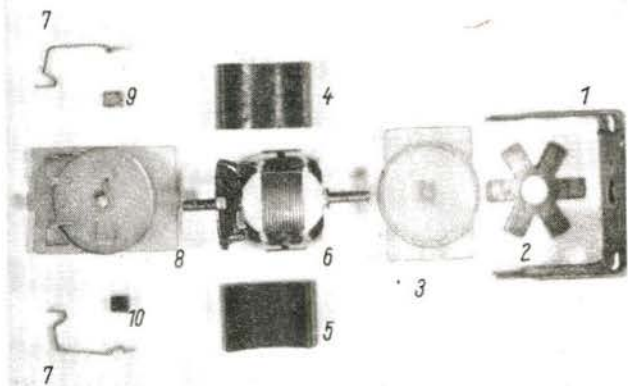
Einzelteile des Motors Typ 6 vom VEB EM Zwickau
